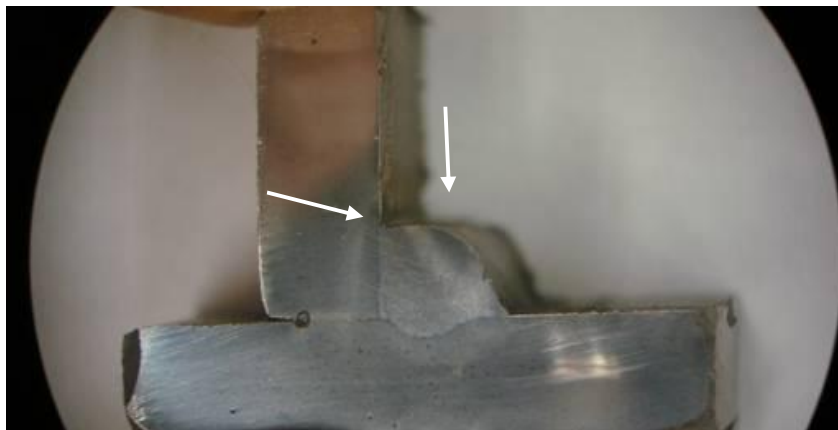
Cordão de solda com pouca fusão na flange CP 73.1.
